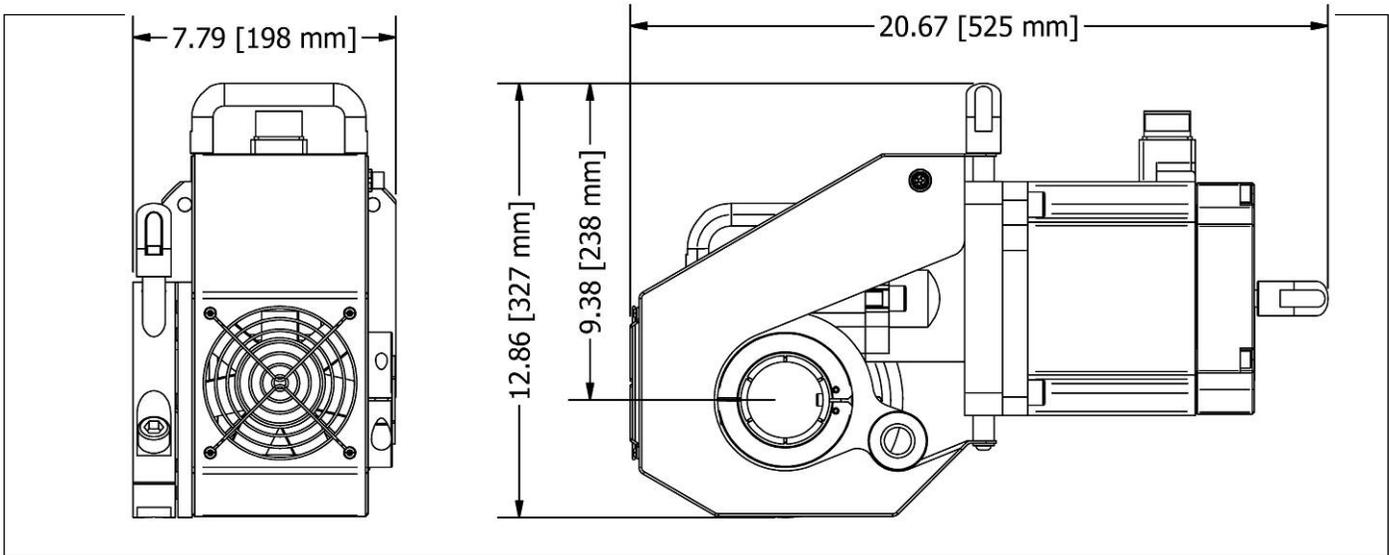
DIMENSIONES MÁQUINA SERVOACCIONADA BB5000
